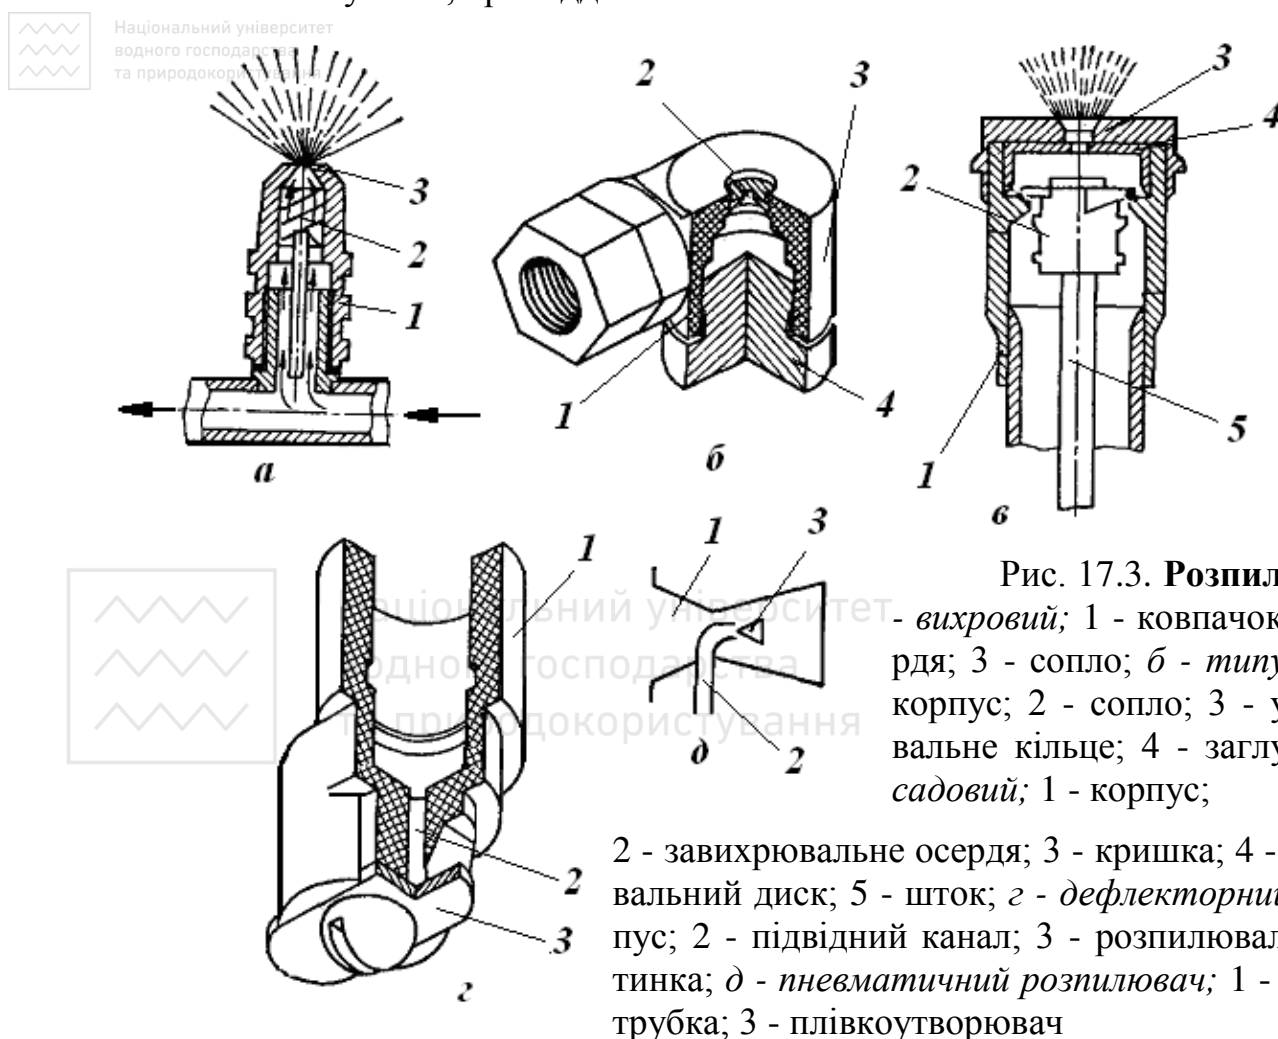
Розпилювачі: а - вихровий; 1 - ковпачок; 2 - осердя; 3 - сопло; б - типу УН; 1 - корпус; 2 - сопло; 3 - ущільнювальне кільце; 4 - заглушка; в - садовий; 1 - корпус;
